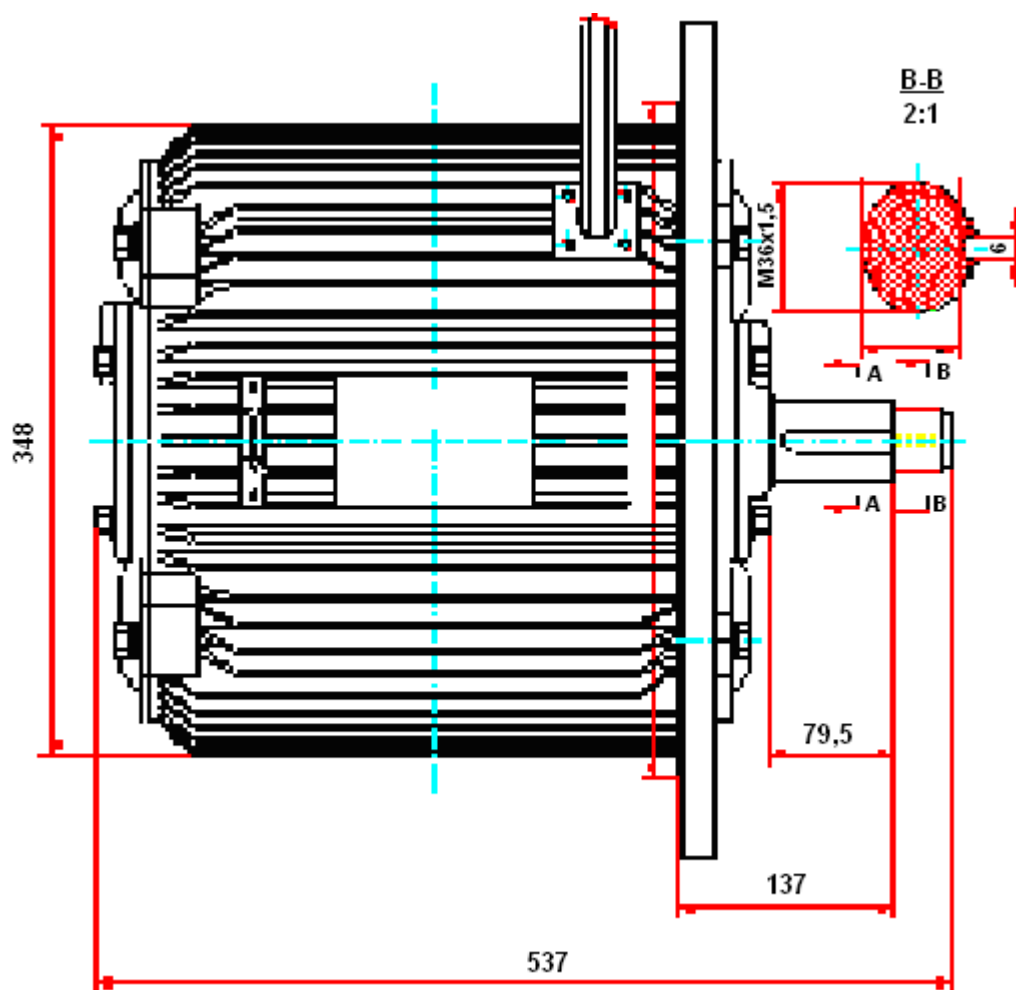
Внешний вид двигателя JD332 и размер установки
